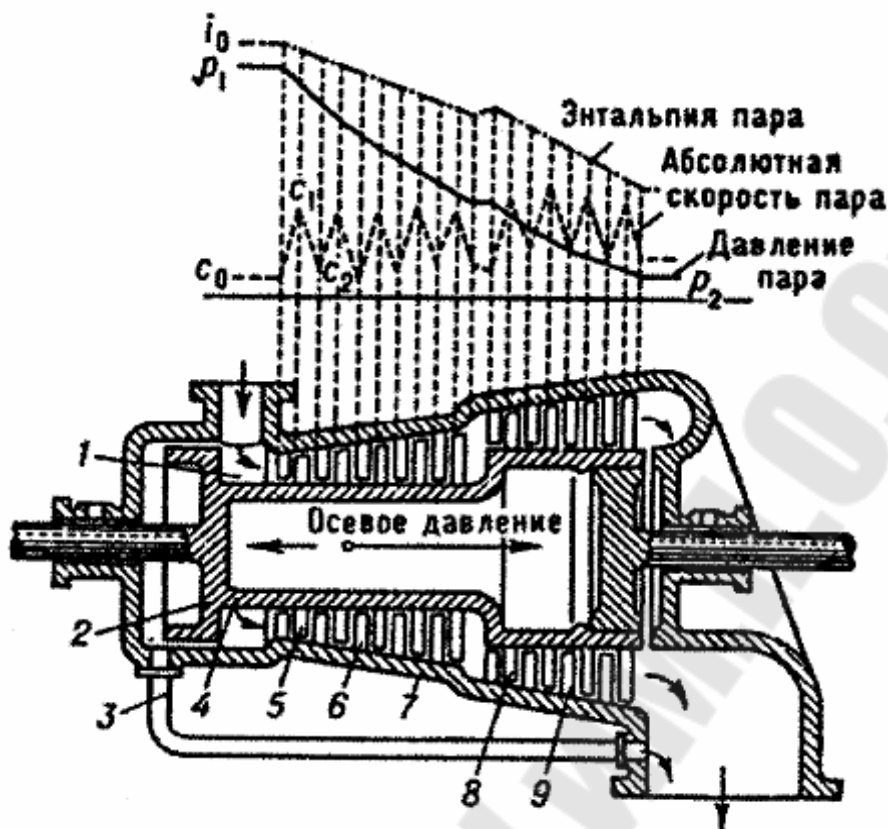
Схематический разрез небольшой реактивной турбины: 1 - кольцевая камера свежего пара; 2 - разгрузочный поршень; 3 - соединительный паропровод; 4 - барабан ротора; 5, 8 - рабочие лопатки; 6, 9 - направляющие лопатки; 7 - корпус.
